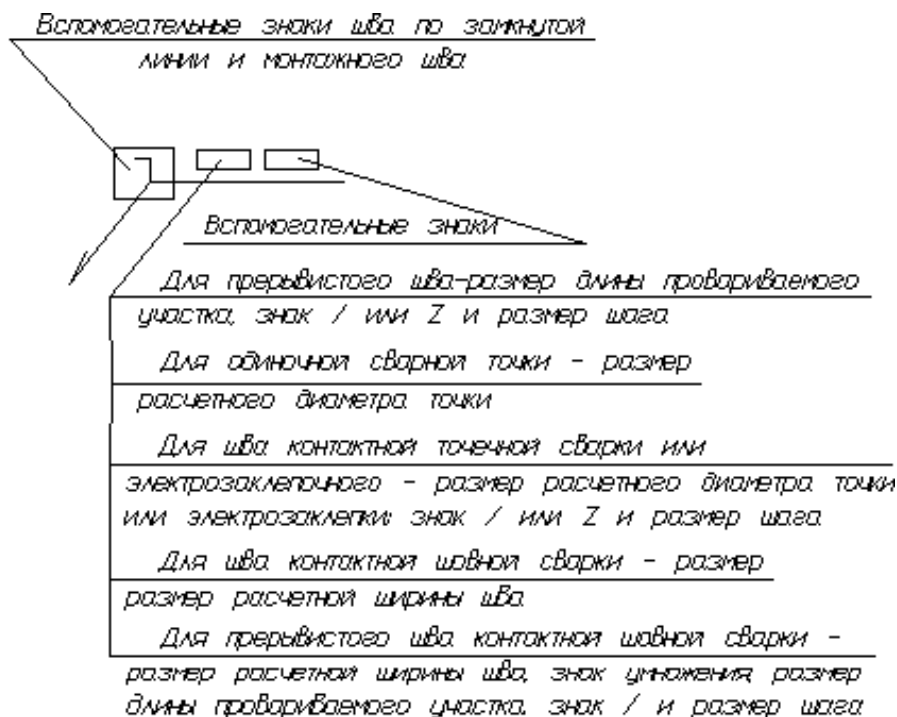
Структура условного обозначения нестандартного шва или одиночной сварной точки
